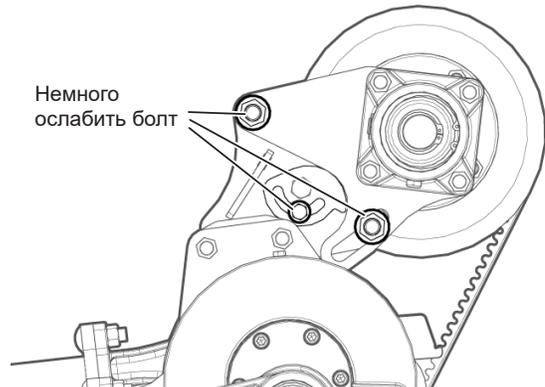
Натяжение ремня ножей: ослабление стопорной гайки и болта.
